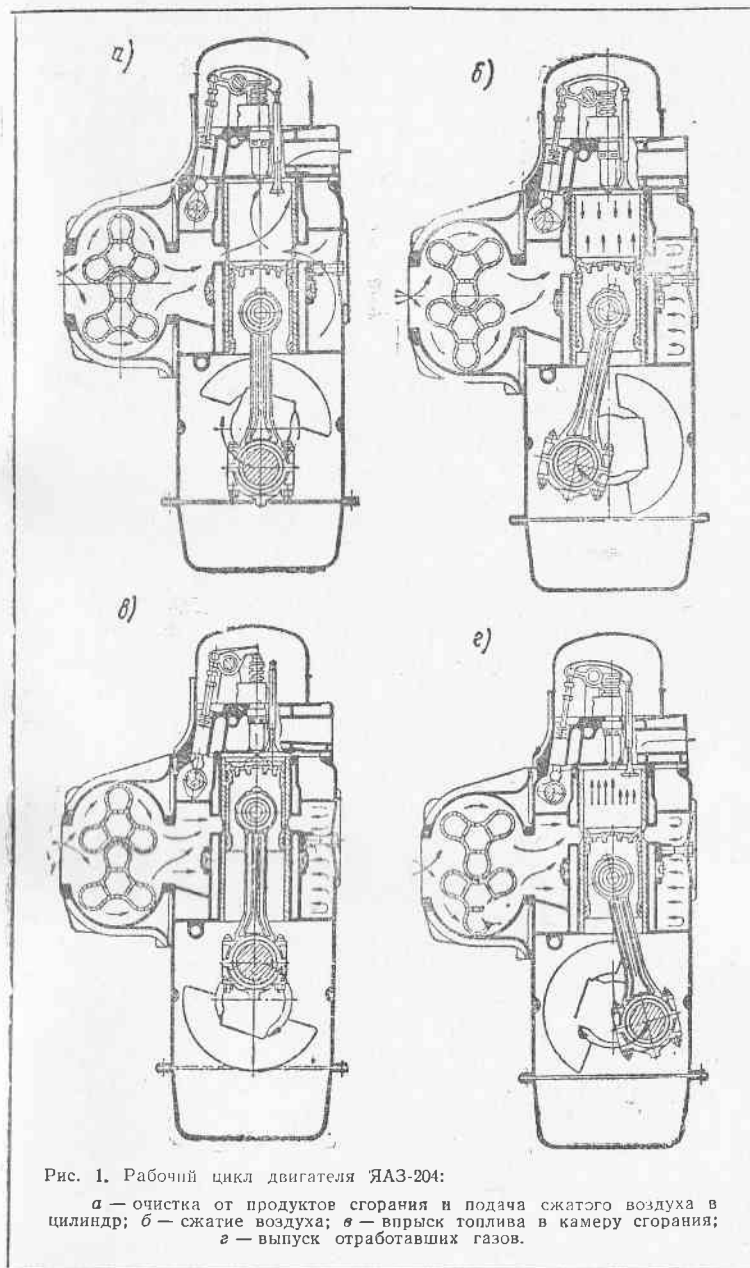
Рабочий цикл двигателя ЯАЗ-204:
